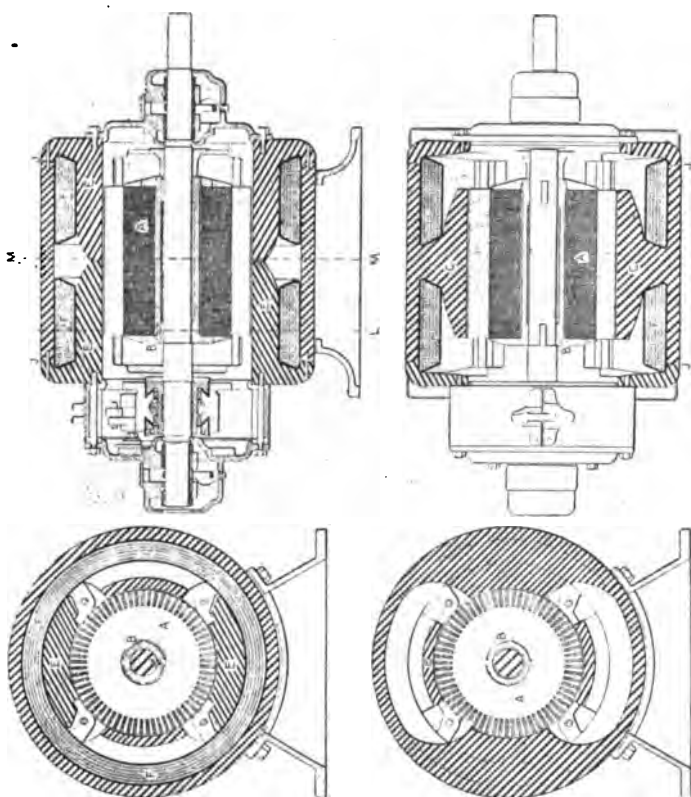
à 5. — Dynamo de la Storey Motor Tool Co pour la commande des machines-outils.
